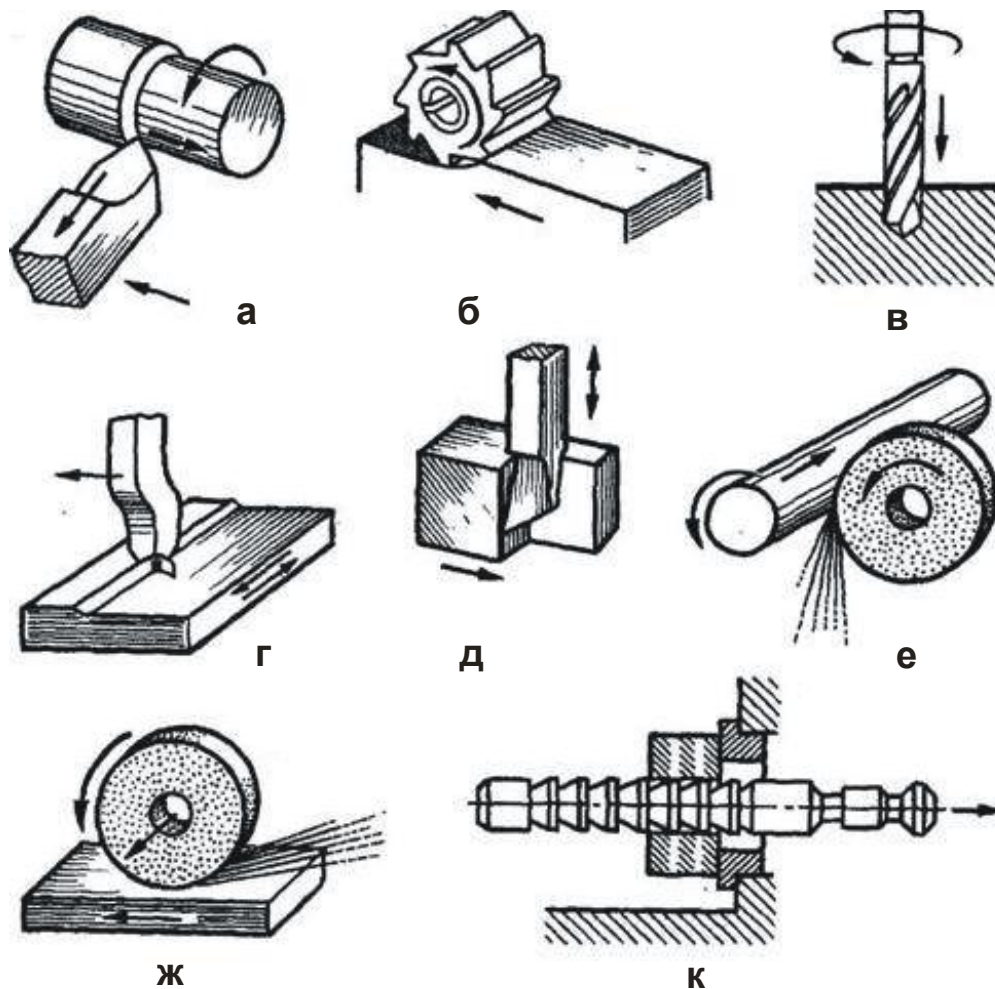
Методи обробки металів різанням: а – точіння; б – фрезерування; в – свердління (зенкерування та розвертання); г – стругання; д – довбання; е – кругле зовнішнє шліфування; ж – плоске шліфування; к – протягування
